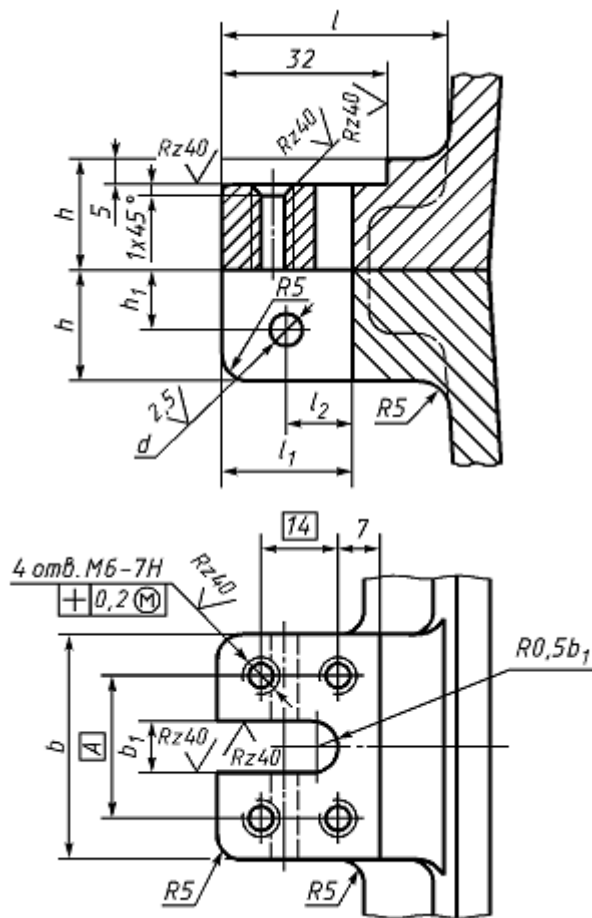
Конструкция и размеры приливов для установки креплений
